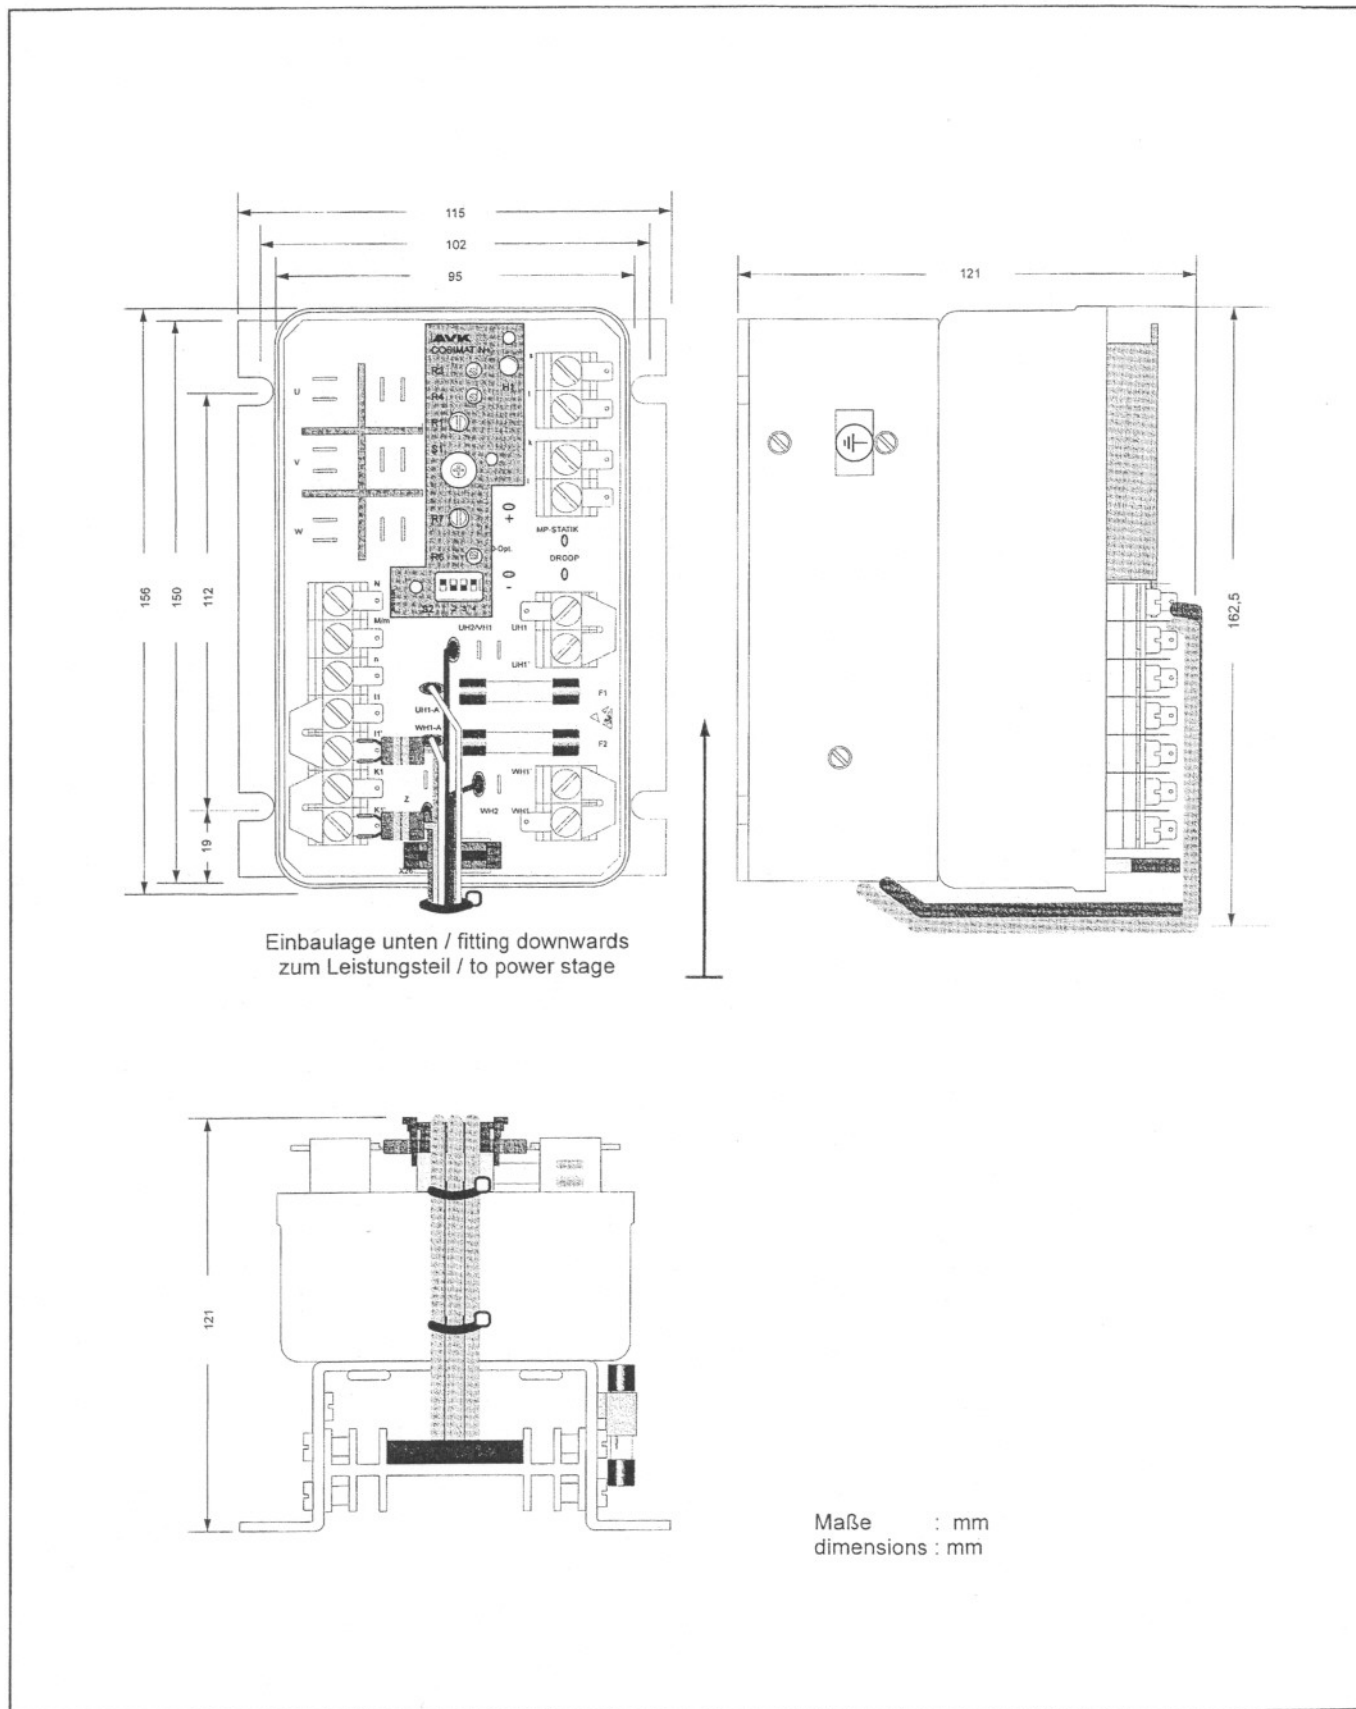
Габаритный чертеж (Рис.25 – Габаритный чертеж)
